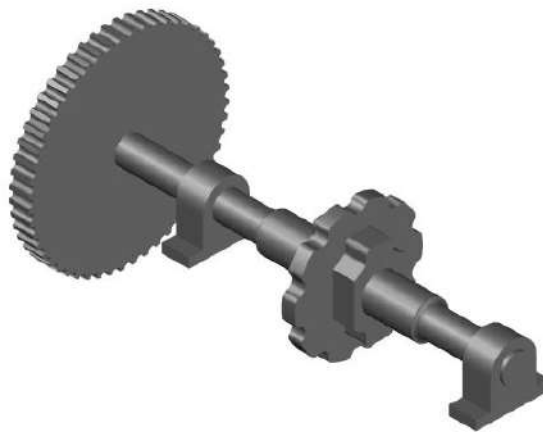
Eje y engranajes en cabezal de mando del redler.
